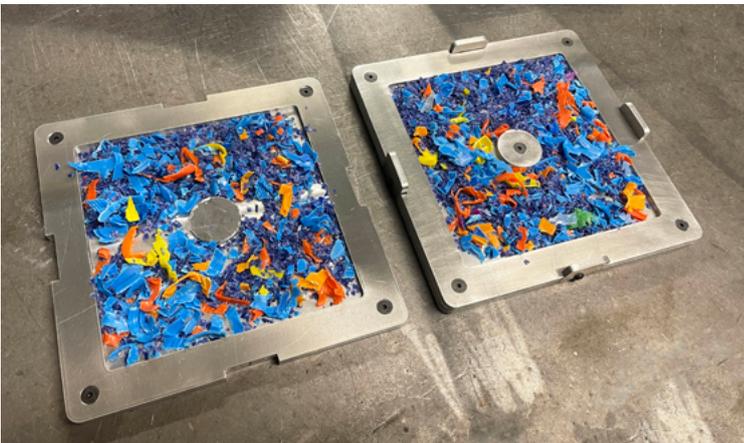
Molde com granulado de plástico antes de ir ao forno. Realizado pela autora
